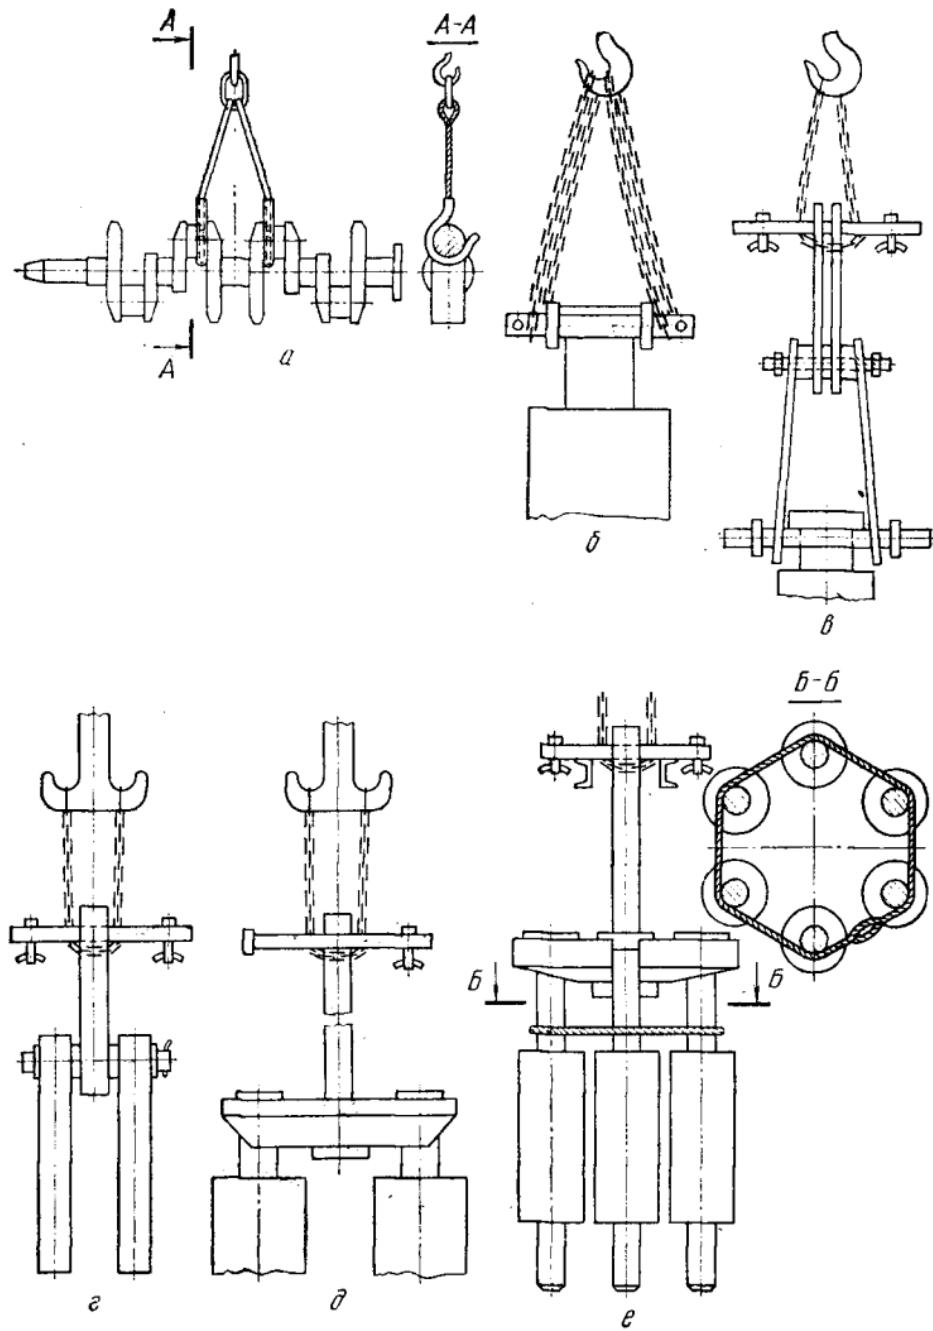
Строповка фигурных валов специальными приспособлениями:
